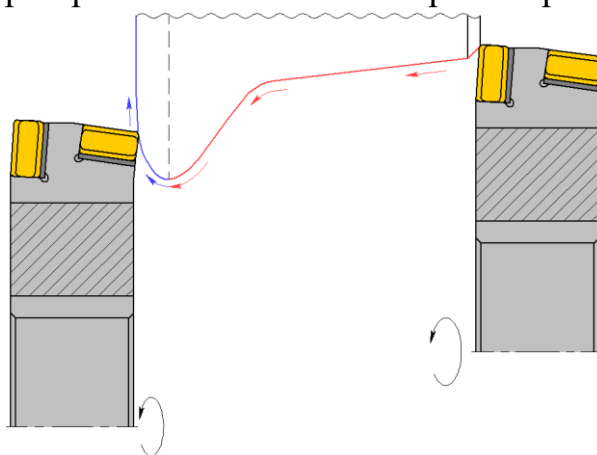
Принцип обработки колесных пар с помощью дисковой фрезы с СМП
